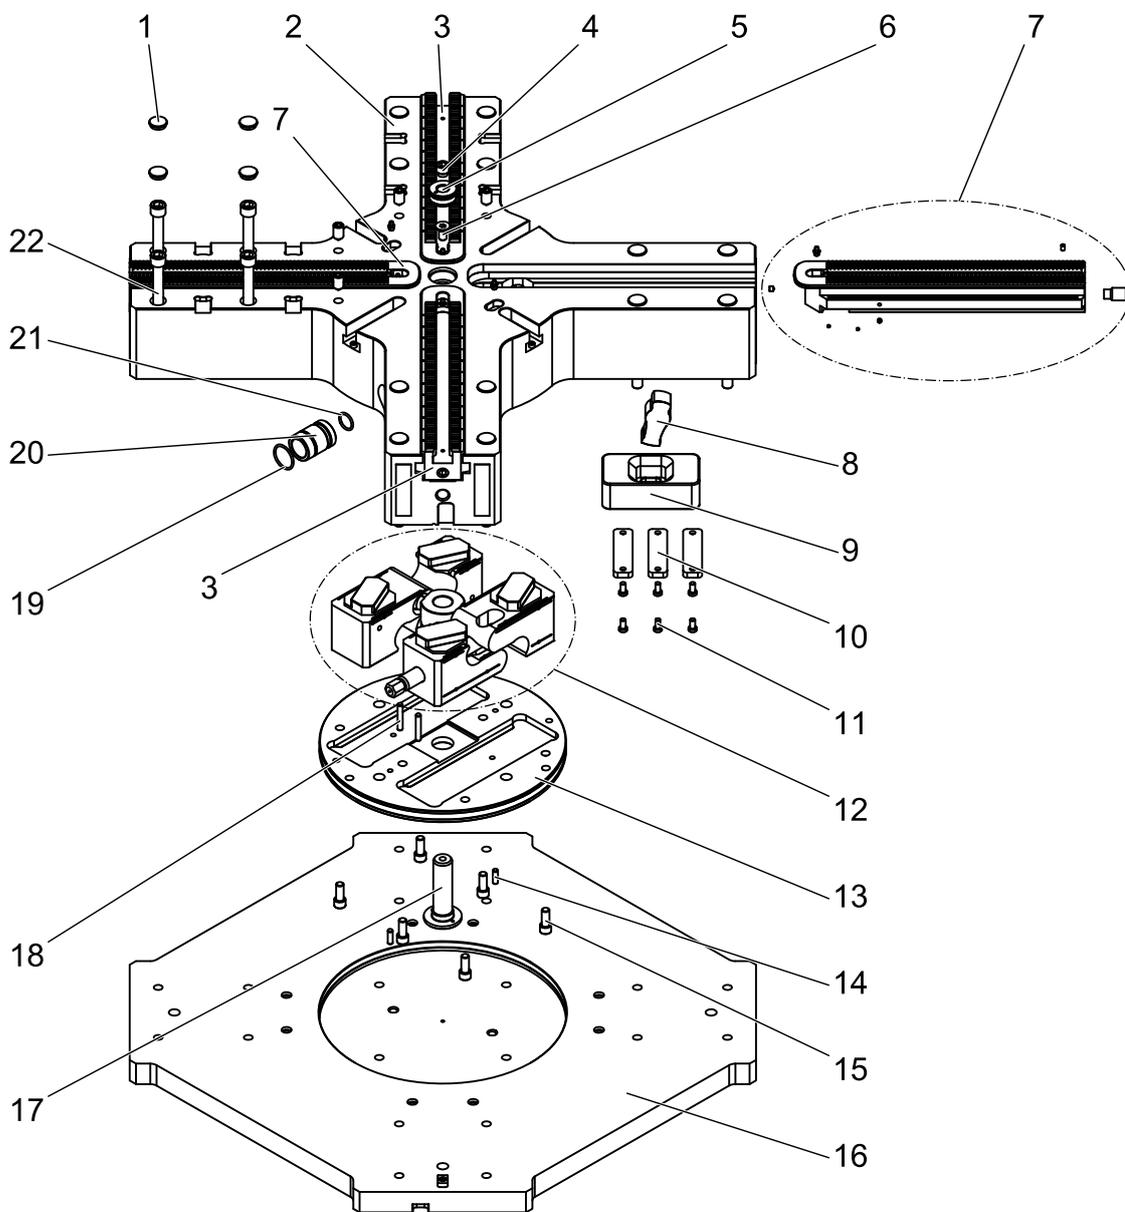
Disassembly / Re-Assembly of the chuck
